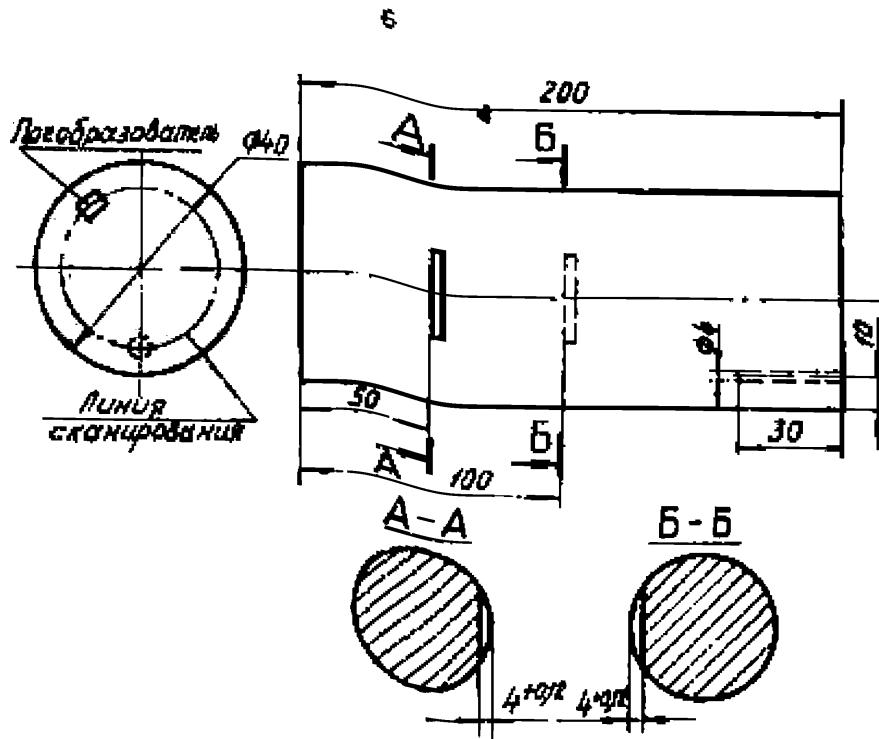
Стандартный образец для настройки ультразвукового прибора при НК элеваторов
